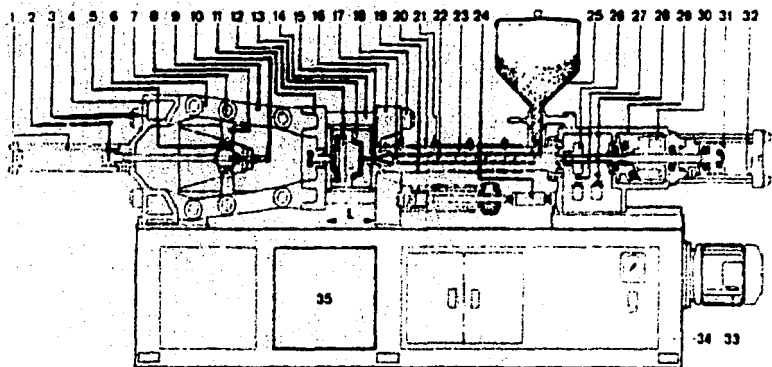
Sección longitudinal de una máquina de moldeo por inyección por husillo recíprocante del tipo doble rodillera. Nótese el molde cerrado y el husillo (22) en posición al final de la inyección. -1. Cilindro hidráulico del molde. -2. Pistón que actúa el cierre del molde. -3. Tuerca de la cabeza de moldes. -4. Cabeza de moldes. -5. Cabeza de cruz. -6. biela corta. -7. Perno. -8. Leva de empuje. -9. Biela larga. -10. Botador de expulsión de las piezas. -11. Platina móvil. -12. Medio molde móvil. -13. Medio molde fijo. -14. Columna. -15. Boquilla libre. -16. Platina fija. -17. Válvula antirretorno. -18. Tuerca de la platina fija. -19. Cilindro para accionar el movimiento del grupo de inyección. -20. Resistencia de calentamiento del cilindro de plastificación. -21. Termopar. -22. Husillo de plastificación. -23. Cilindro de plastificación. -24. Tuerca para regulación de la posición de la boquilla. -25. Tolva. -26. Acoplamiento. -27. Interruptor de límite para accionar la segunda presión de inyección. -28. Interruptor de límite para actuar el término de la plastificación. -29. Cabeza de inyección. -30. Motor hidráulico para actuar la rotación del husillo. -31. Pistón de inyección. -32. Cilindro de inyección. -33. Motobomba del sistema hidráulico. -34. Bancada. -35. Abertura para recolectar las piezas moldeadas.
